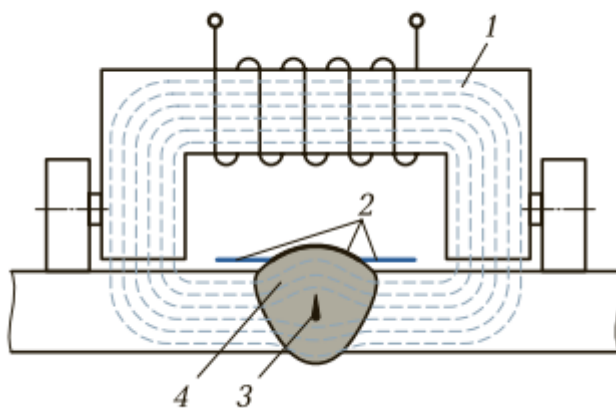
Схема магнитографического контроля: 1 — намагничивающее устройство; 2 — магнитная пленка; 3 — дефект; 4 — сварной шов
